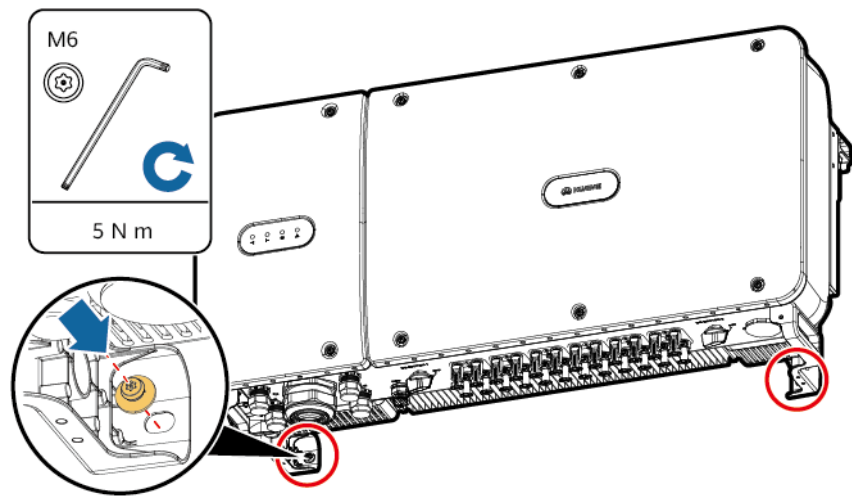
Montaggio del SUN2000 su una staffa di montaggio
